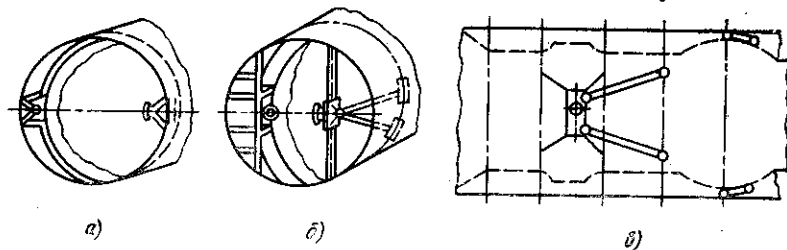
Конструктивные схемы установки узлов крепления двигателей внутри фюзеляжа
